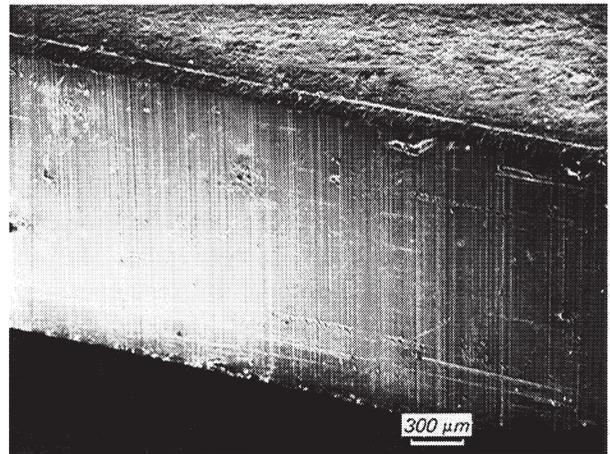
REM-Aufnahme einer feingeschnittenen Fläche
